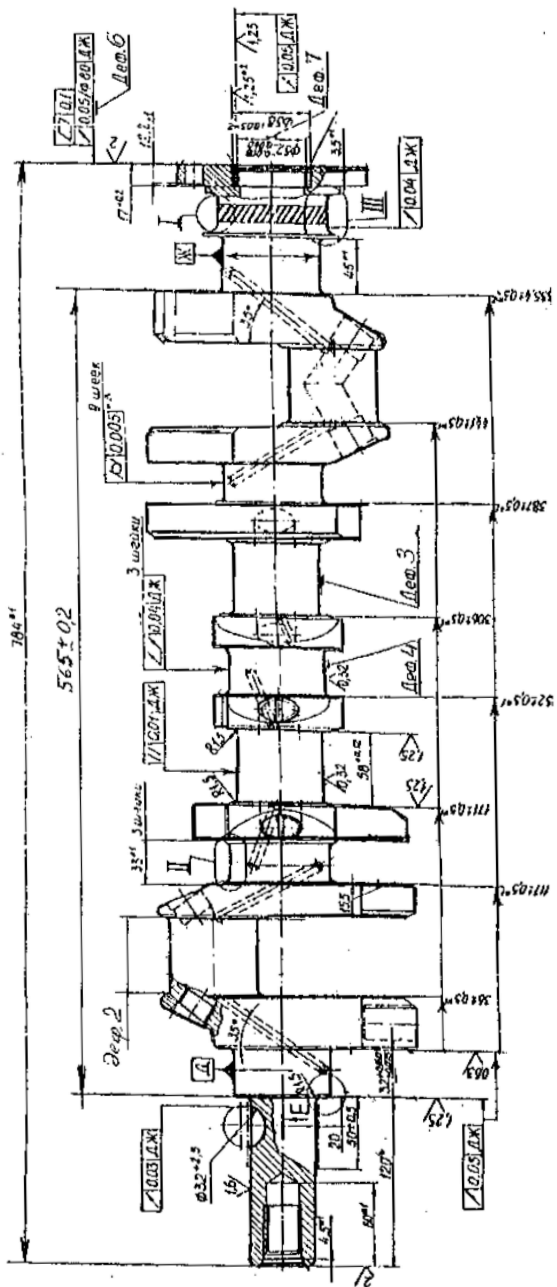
Коленчатый вал двигателя ЗИЛ-130. Материал: Сталь 45. Твердость шеек НРС 52-62
